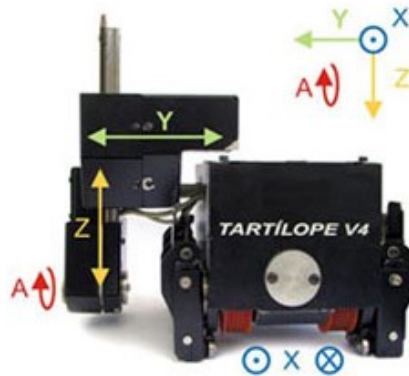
Manipulador Tartílope V4. Fonte: SPS – Sistemas e Processos de Soldagem [51].
